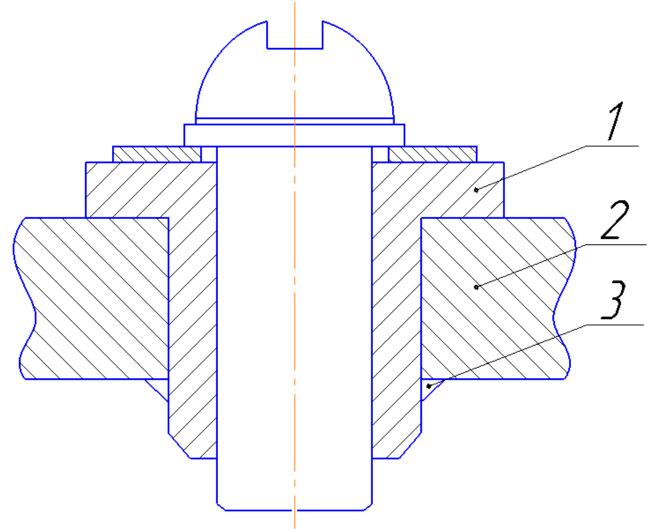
Увеличение длины резьбового отверстия привариванием втулки [2]: 1- втулка; 3- заготовка; 3- сварной шов
